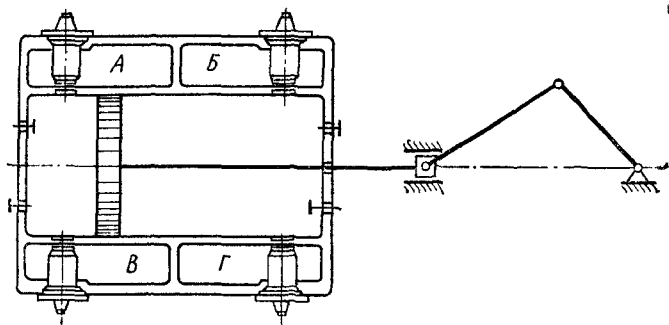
Схема конструкции компрессора с полостями дополнительного мертвого пространства, расположенными в корпусе цилиндра
